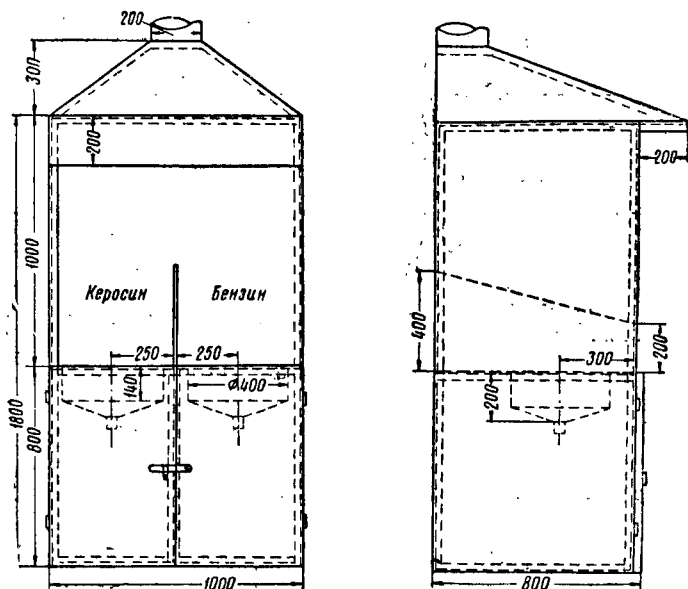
Вытяжной шкаф для промывки роликовых подшипников
